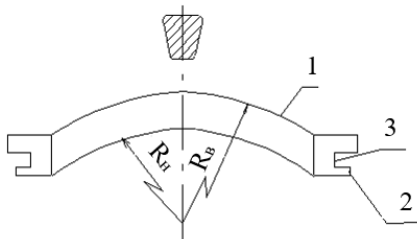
Конструкція колосника з трапецеїдальною формою робочої частини: 1 – робоча частина; 2 – головка колосника; 3 – зів для кріплення колосника;  $R_b$  – радіус постійної кривизни верхньої поверхні;  $R_n$  – радіус постійної кривизни нижньої поверхні
